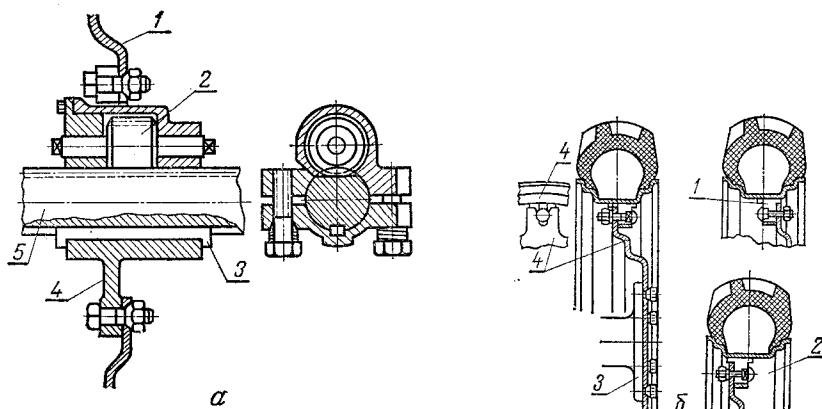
Схема регулирования ширины колеи трактора ручным способом: а — перемещение ступицы колеса по полуоси червячным механизмом: 1 — диск; 2 — червяк; 3 — шпонка; 4 — ступица; 5 — полуось; б — изменение положения обода относительно диска и диска относительно фланца полуоси: 1 — стойка на обode; 2 — обод; 3 — фланец полуоси; 4 — диск.
